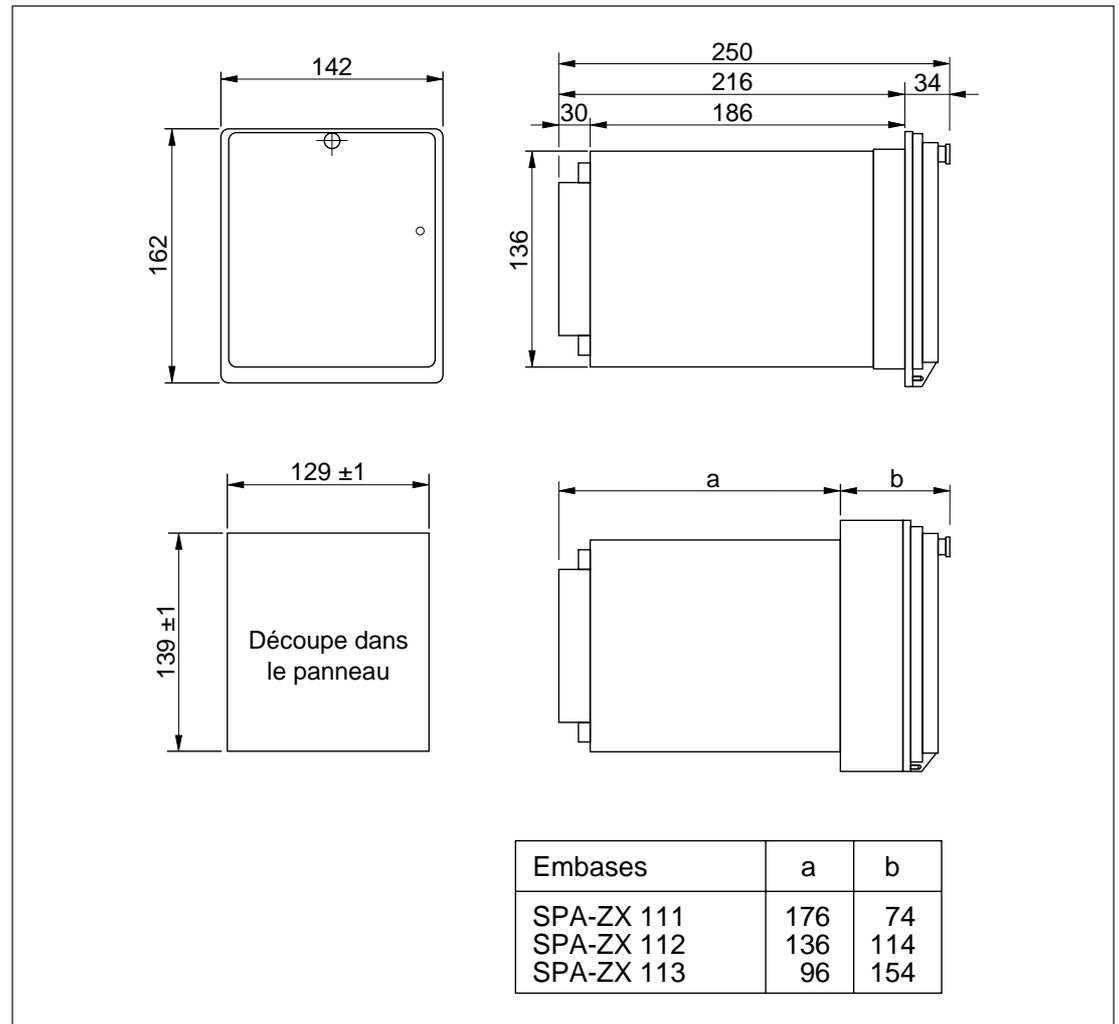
Dimensions du relais de protection SPAJ 110 C.
